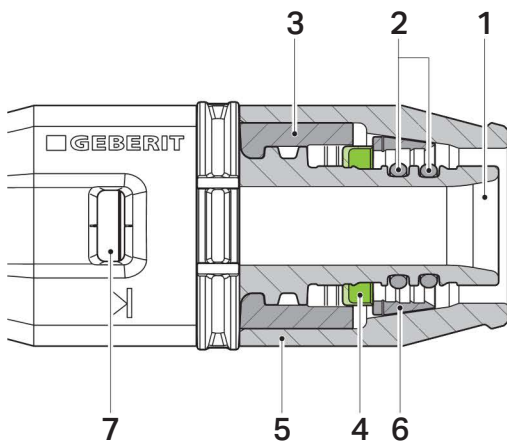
Geberit PushFit Steckverbindung vor dem Stecken
